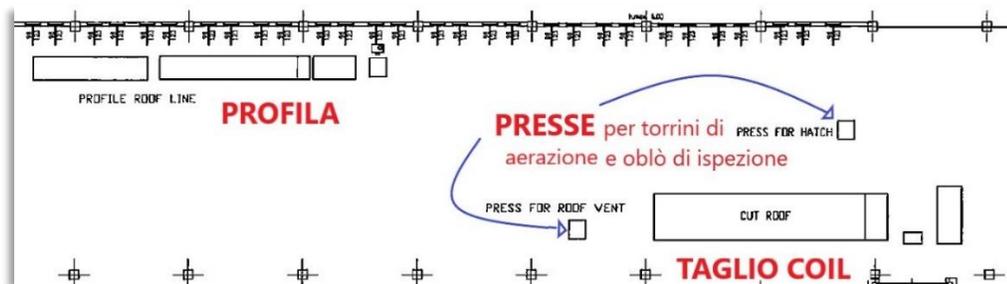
layout del reparto per la realizzazione degli spicchi tetto
